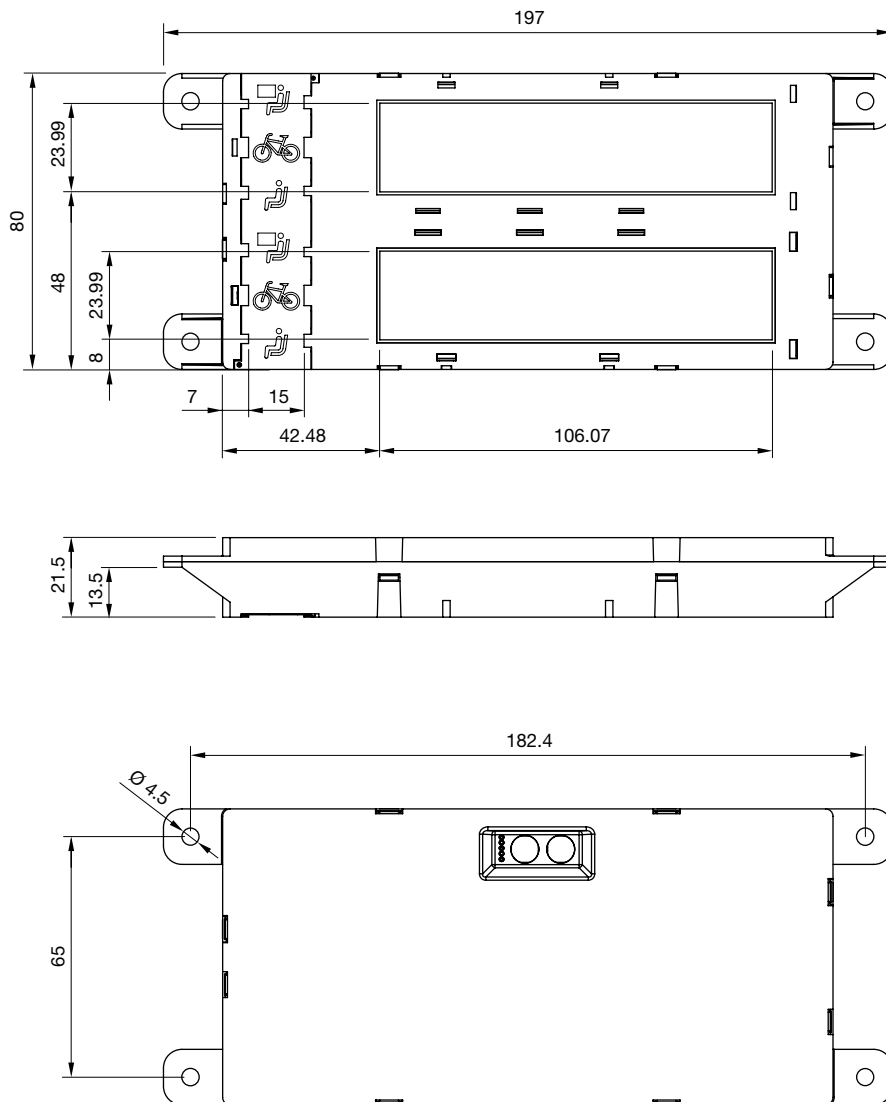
Abmessungen (mm) Gehäuse mit zwei Displays.
